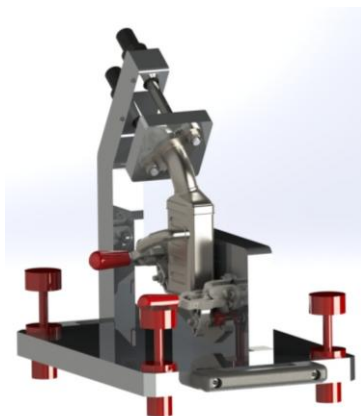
Utillaje de soldadura láser de fase 4.
